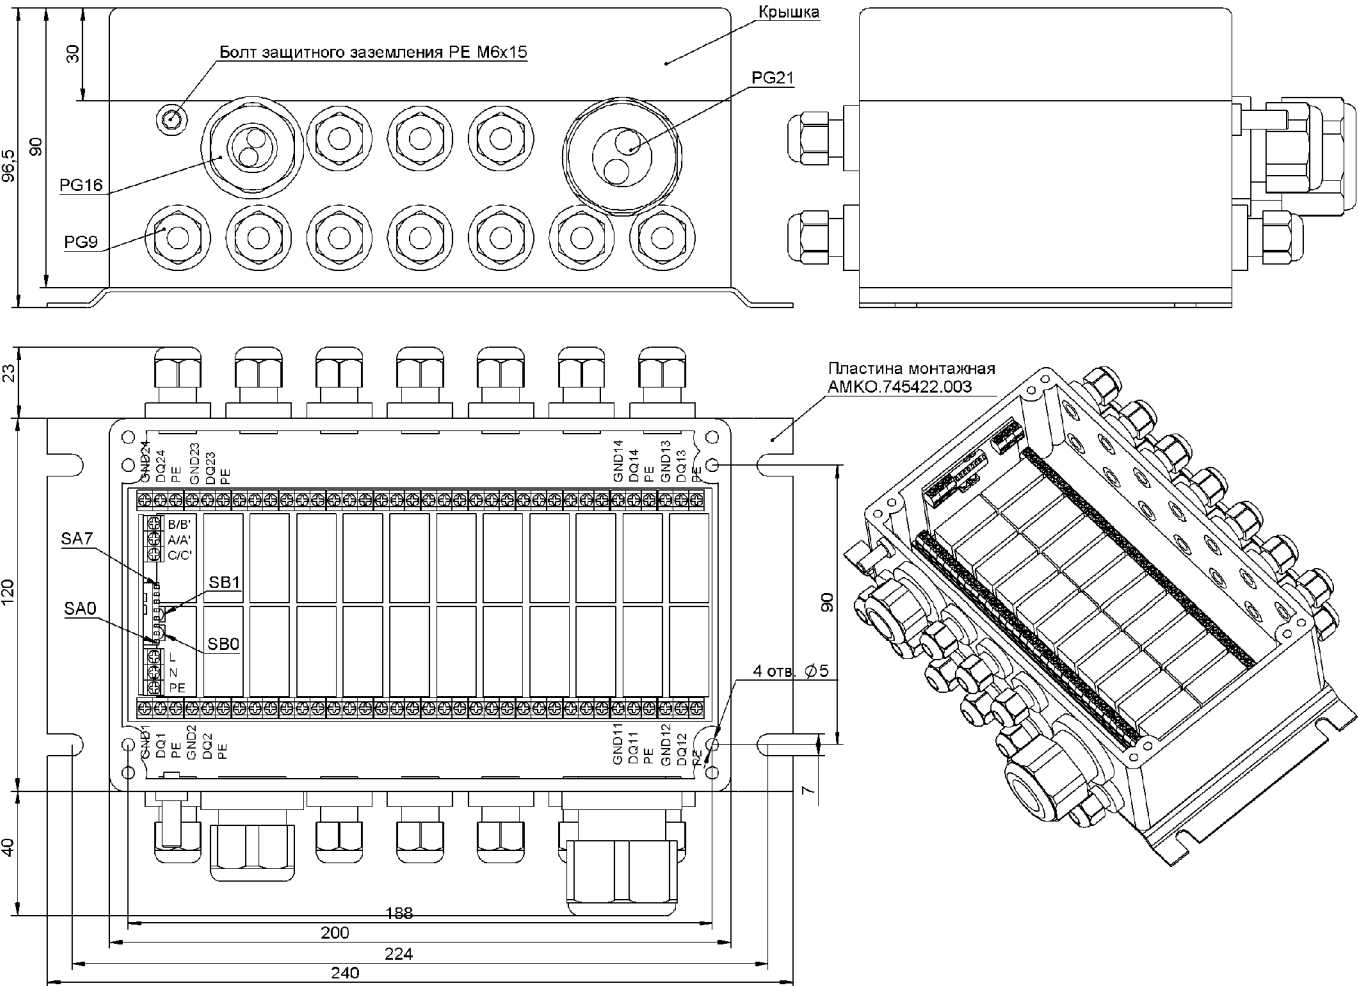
Габаритный чертеж контроллера - термопреобразователя MB-1W24
